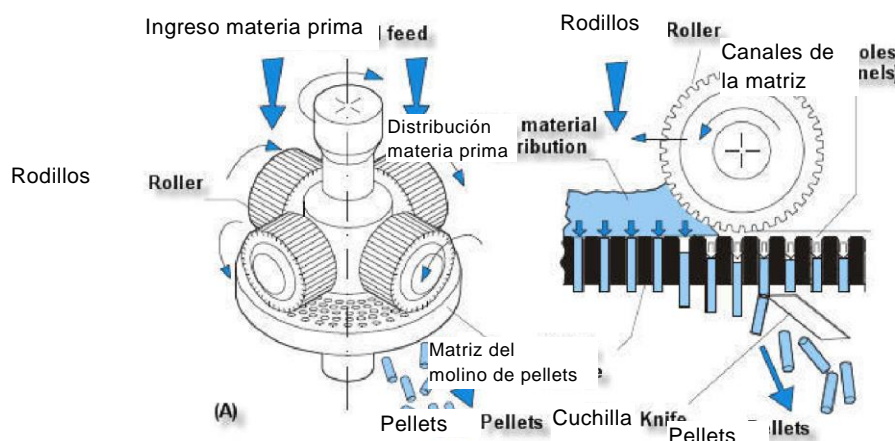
Vista esquemática de un molino de pellets de matriz plana. Fuente: Safety Engineering³
